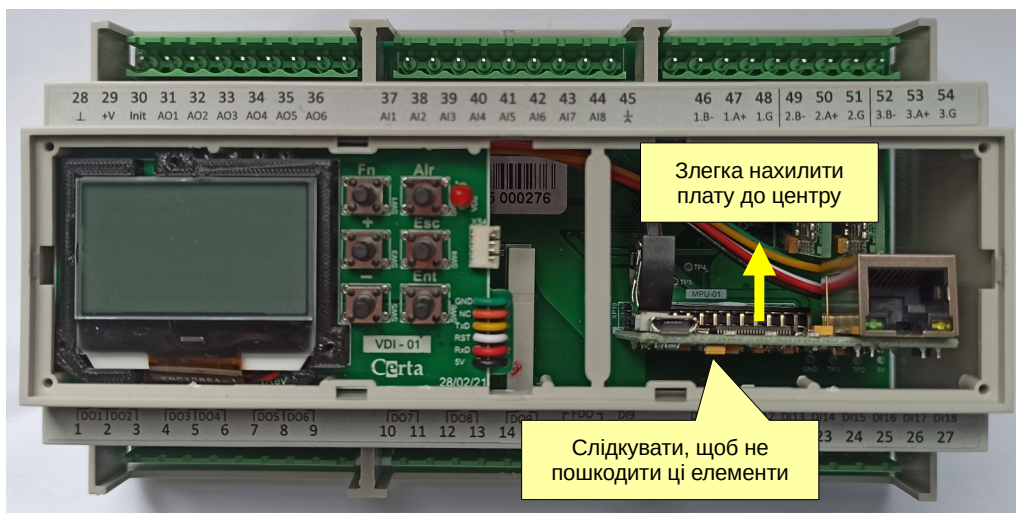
Вставлення плати BASE в корпус (вид згори)
